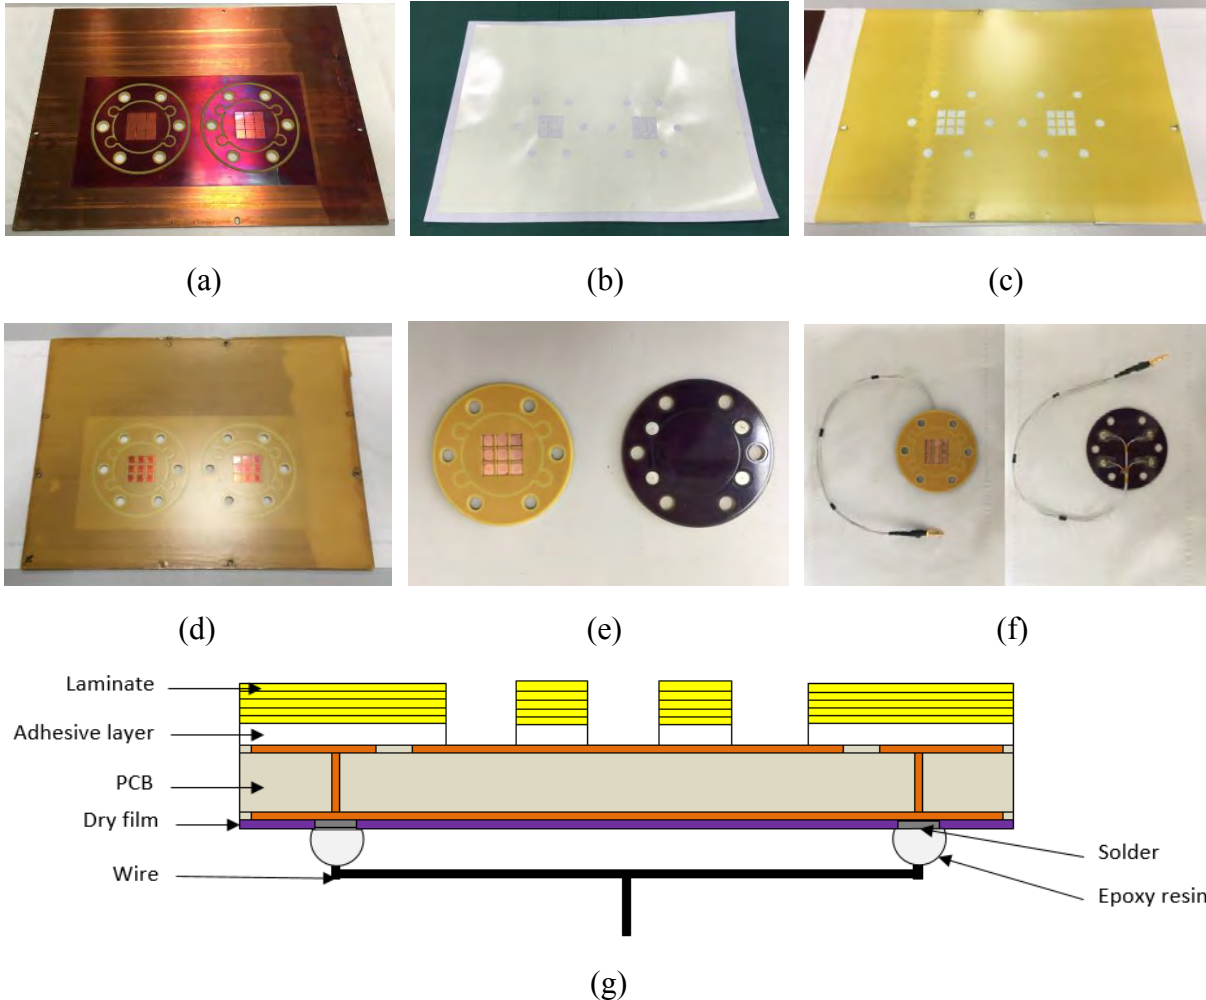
PCB (a), colle acrylique (b) et laminé (c) après thermo-compression (d), détournage (e) et câblage (f) ainsi qu'un schéma en vue de coupe (g)
